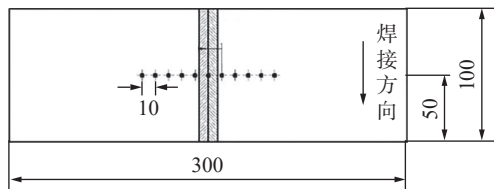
测量焊接残余应力的取点位置 (mm)
